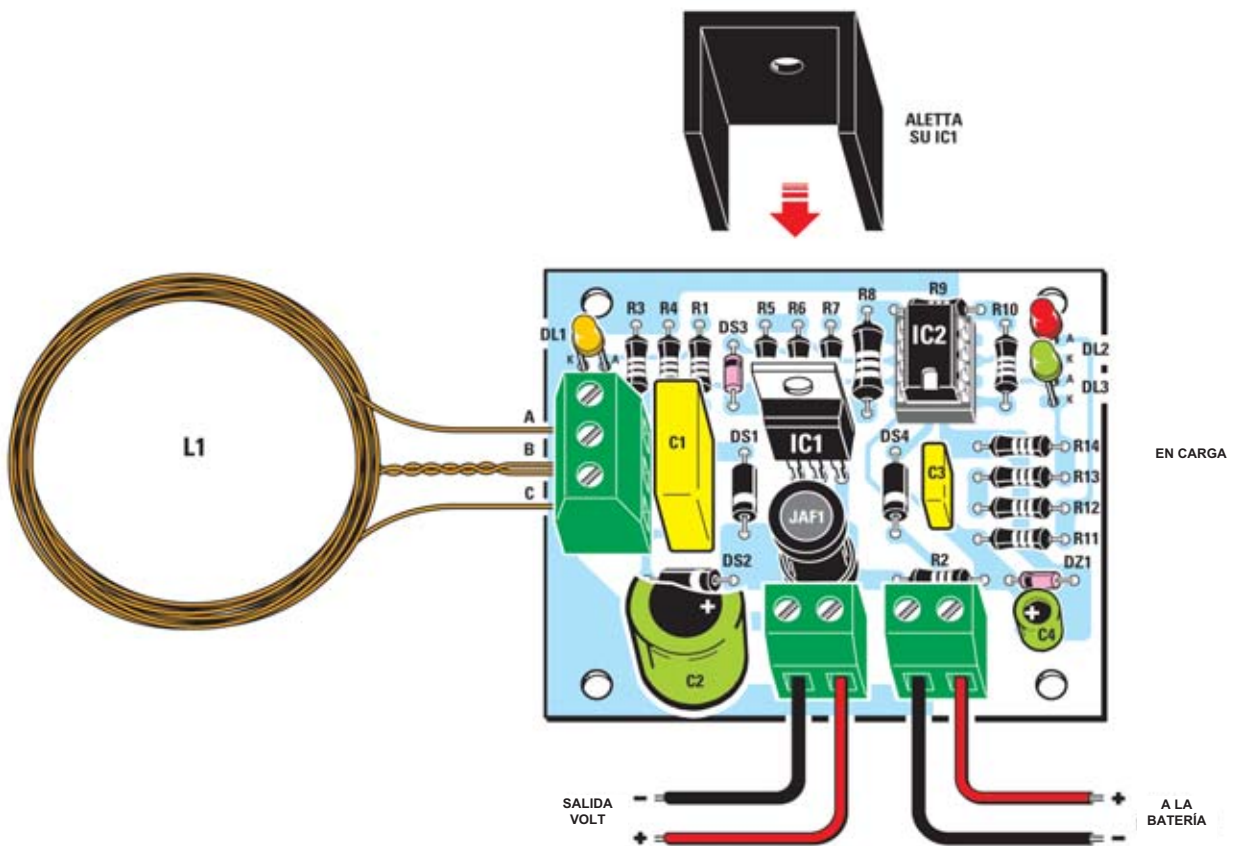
Esquema de montaje de la tarjeta del receptor. En este caso, hay que fijar el integrado IC1 sobre el disipador de calor antes de soldar los terminales en los agujeros en el centro de la placa.
